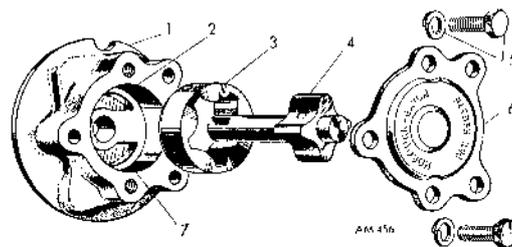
Die direkt vom hinteren Nockenwellenende angetriebene und zwischen Motorblock und Schwungrad liegende Ölpumpe wird hier zerlegt wiedergegeben. Es bedeuten: 1 Pumpengehäuse, 2 Auslaßöffnung, 3 äußerer Rotor, 4 innerer Rotor, 5 Befestigungsschraube und Federring, 6 Pumpendeckel, 7 Saugöffnung
